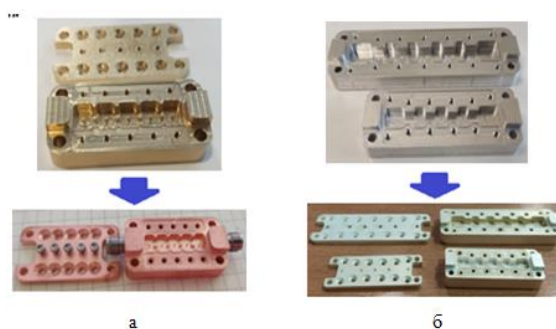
Образцы ранее рассчитанных ППФ второго типа с различным технологическим процессом производства: а – латунный корпус, покрытый медью; б – алюминиевый корпус покрытый медью и серебром
